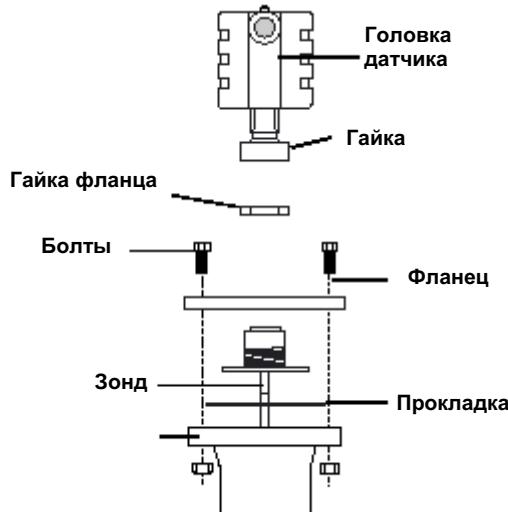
Установка в резервуаре с незакрепленным фланцем ("пластинчатая форма")
